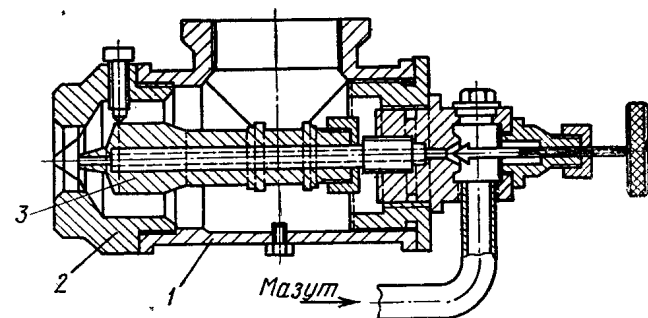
Форсунка низкого давления конструкции Стальпроекта:
